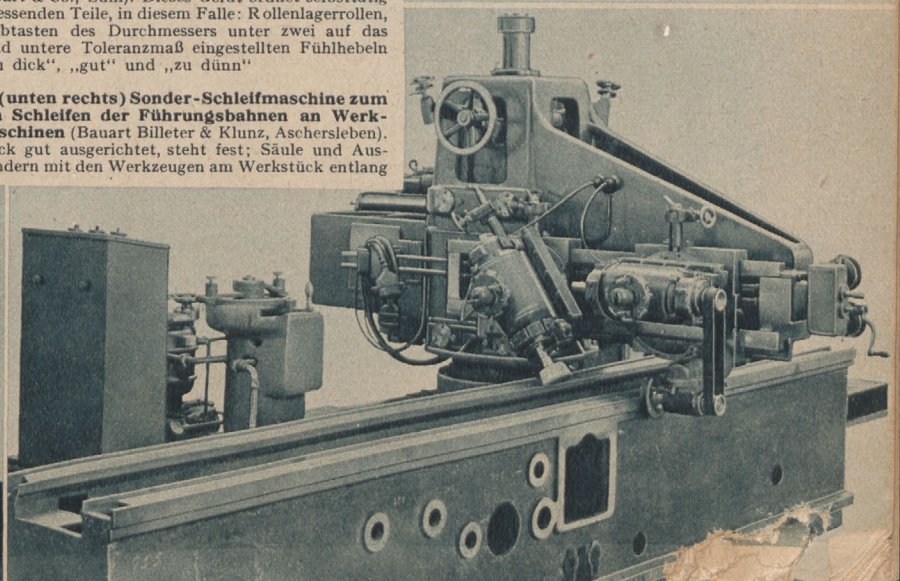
(unten rechts) Sonder-Schleifmaschine zum genauen Schleifen der Führungsbahnen an Werkzeugmaschinen (Bauart Billeter & Klunz, Aschersleben). Werkstück gut ausgerichtet, steht fest; Säule und Ausleger wandern mit den Werkzeugen am Werkstück entlang
